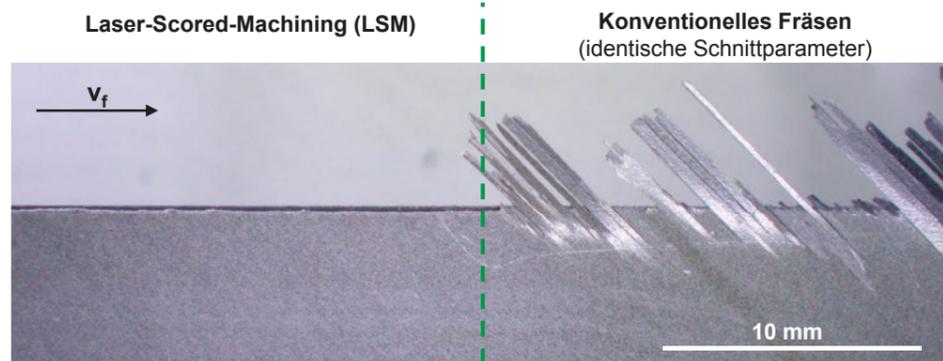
CFK-Bauteilkante, bearbeitet mit verschlissenem Fräser durch Laser-Scored-Machining (LSM) und konventionelles Fräsen
